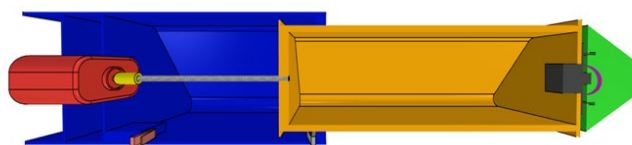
Модель сборки разрабатываемой посадочной опоры
